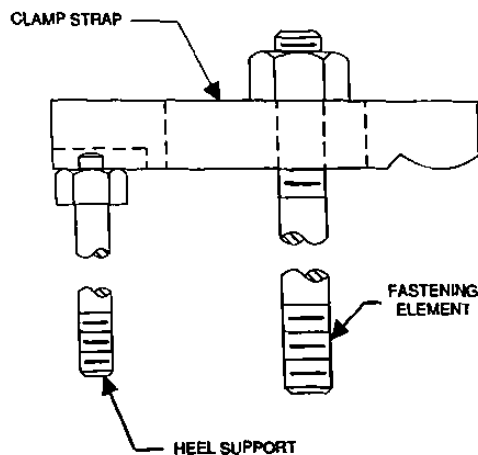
Los elementos importantes para el ensamble de un sujetador de placa son la placa, ensamble o elemento de sujeción, y el apoyo.
